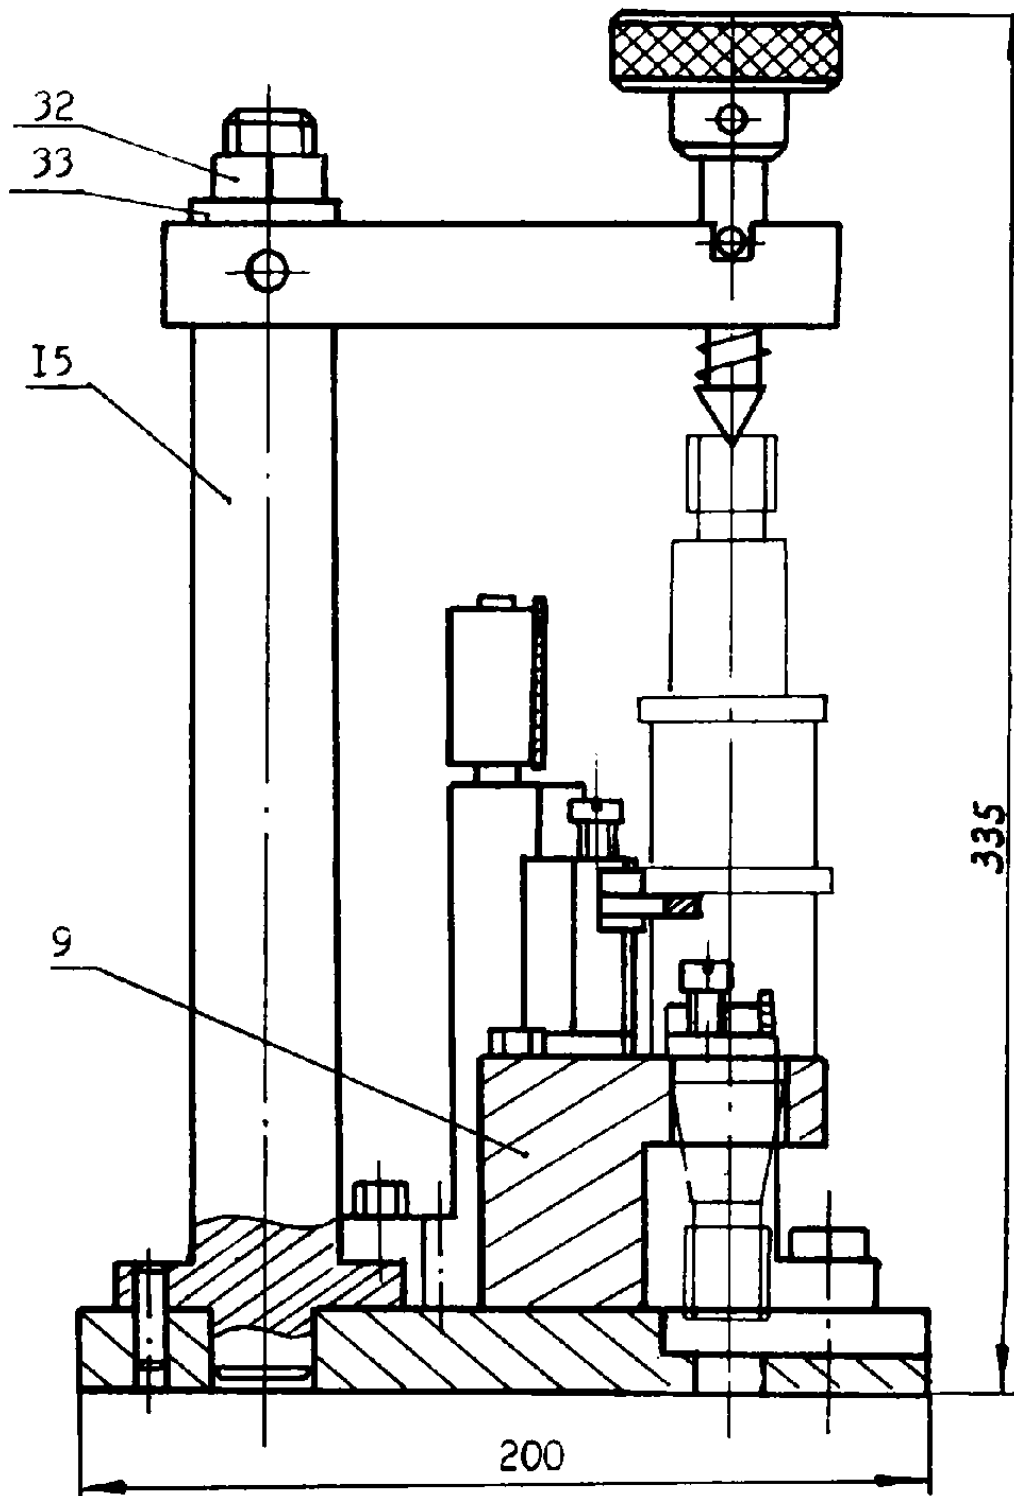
а – Багатомірний пристрій для контролю лінійного розташування шийок валів
